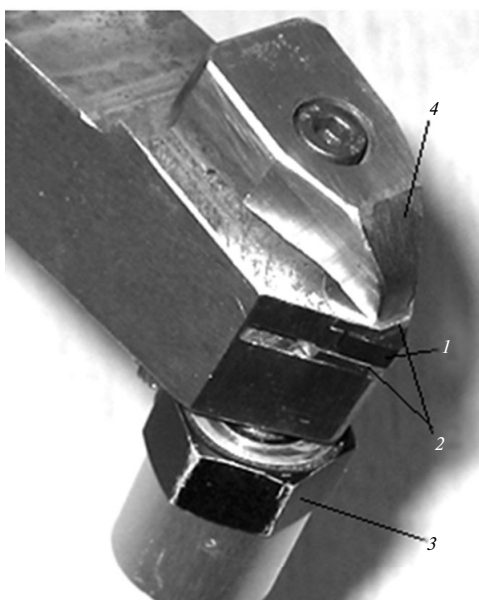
Резец со вставками из высокодемпфирующих материалов: 1 – режущая пластина из КНБ; 2 – вставки из демпфирующего материала; 3 – акселерометр; 4 – прихват.
